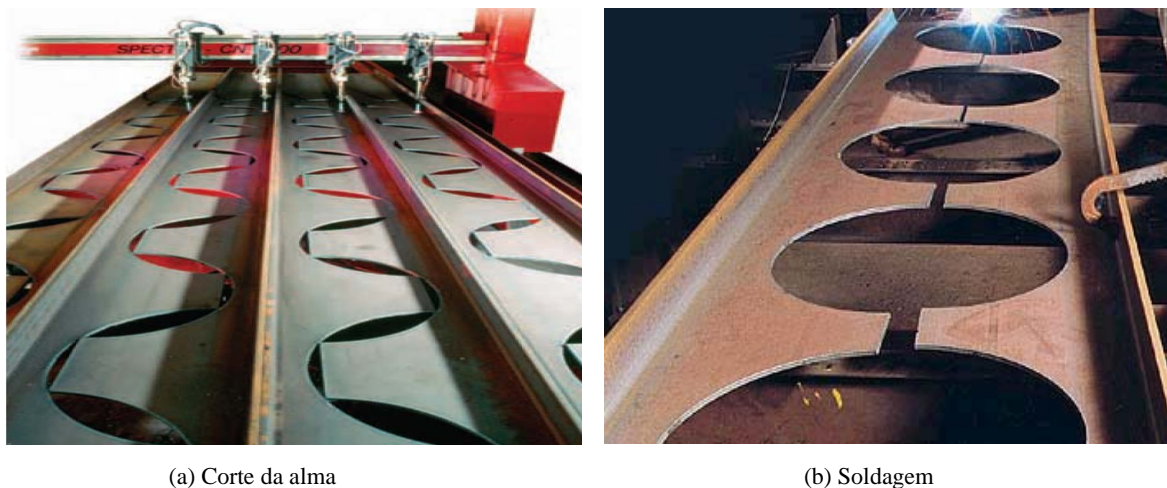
Fabricação de vigas celular (fonte: www.asdwestok.co.uk – acessado em 14/09/2010)
